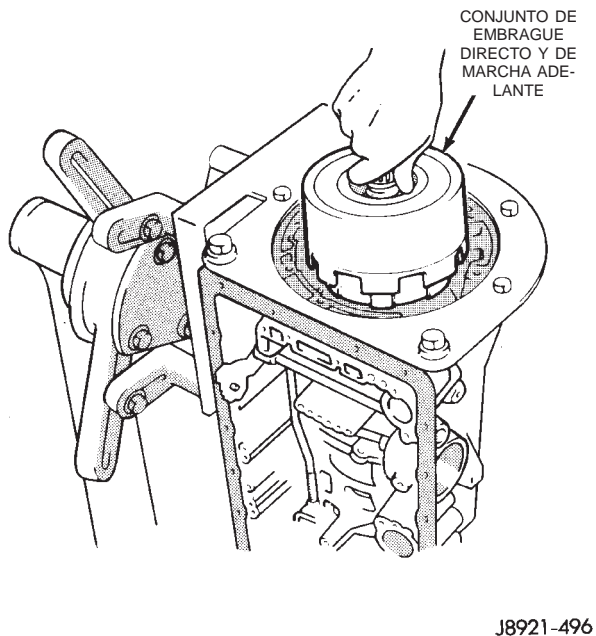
Desmontaje del conjunto de embrague directo y de marcha adelante
